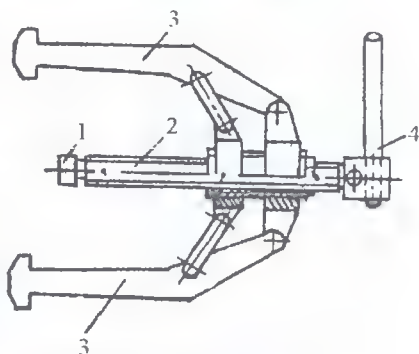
Универсальный винтовой съемник: 1 — упор; 2 — винт; 3 — захват; 4 — рукоятка
